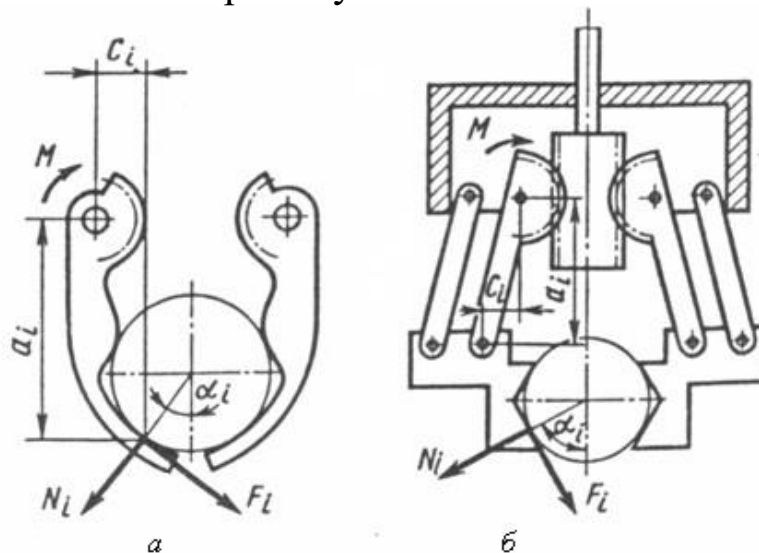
Схемы для расчета моментов, удерживающих заготовку в ЗУ: *а* – с поворотом губок; *б* – с плоскопараллельным движением губок
